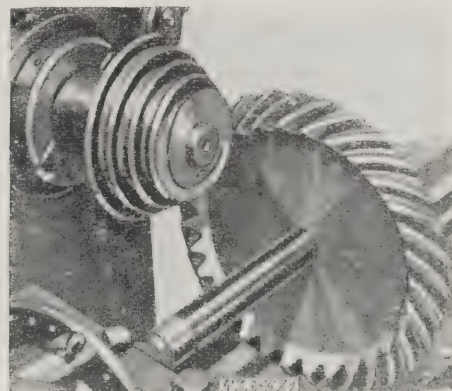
Schraubwälzgetriebe mit Kegelrädern.
